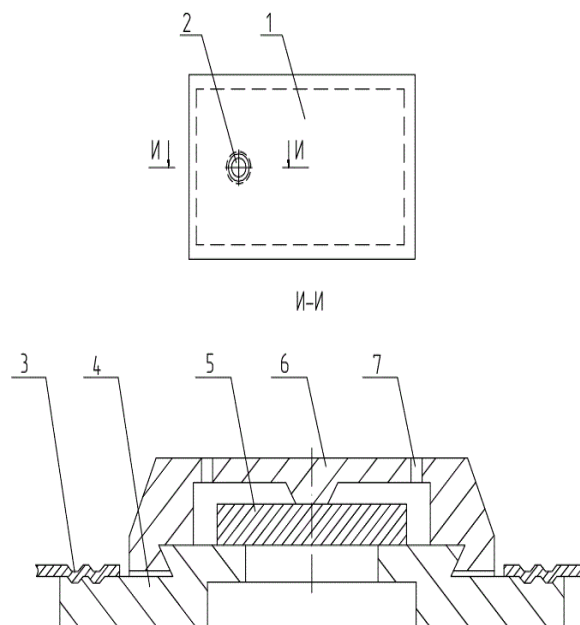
Упаковка из ламината РТЕ/РЕ с выпускным клапаном
